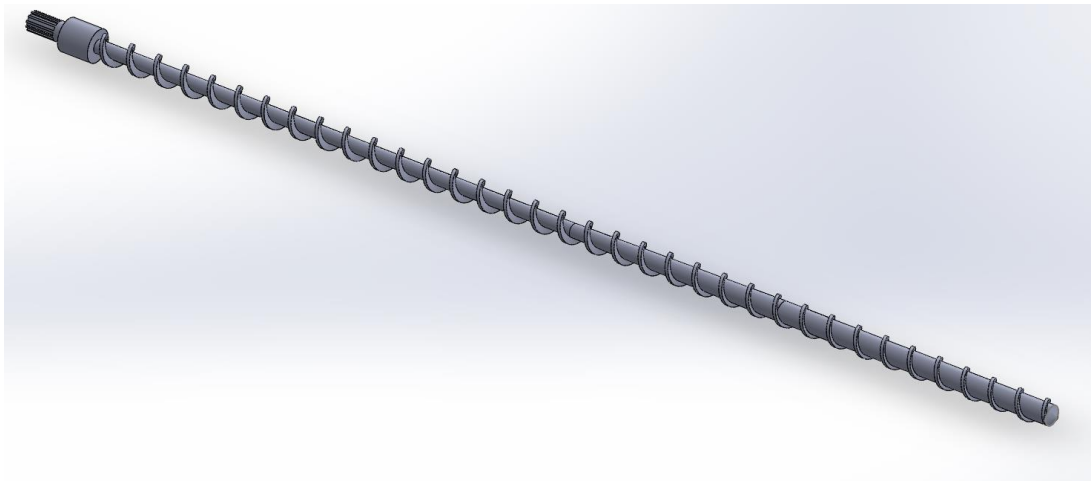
Готова модель базової конструкції черв'яка.
